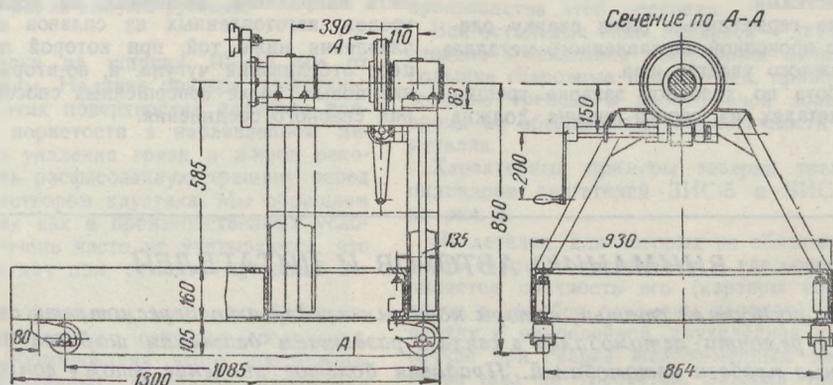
Универсальный стенд для разборки и сборки двигателя.
